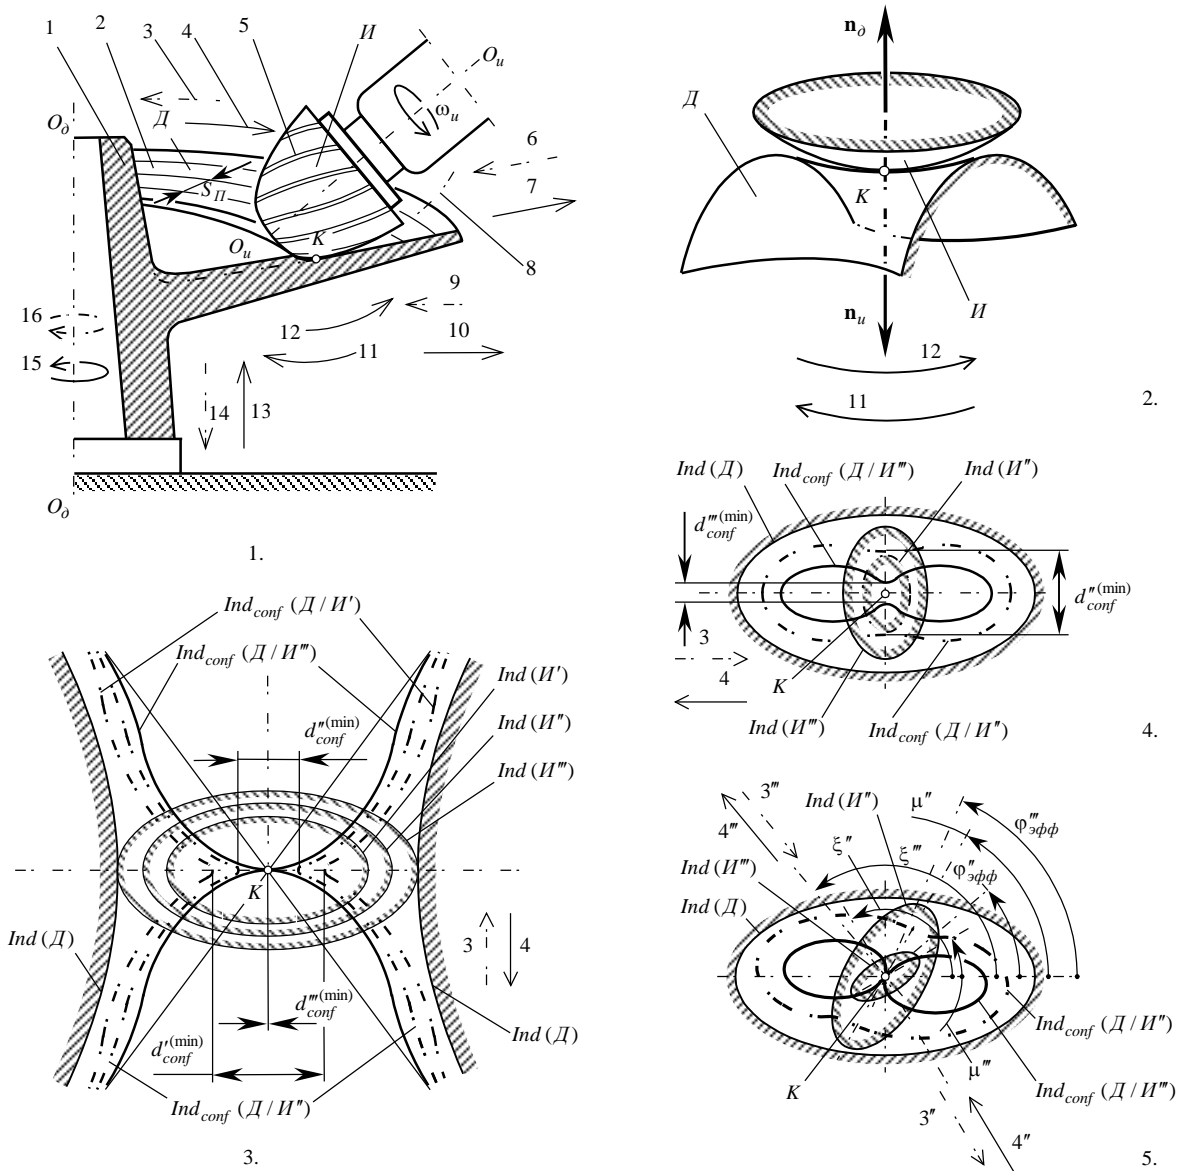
Схема способа обработки сложных поверхностей деталей (а.с. №1249787).
